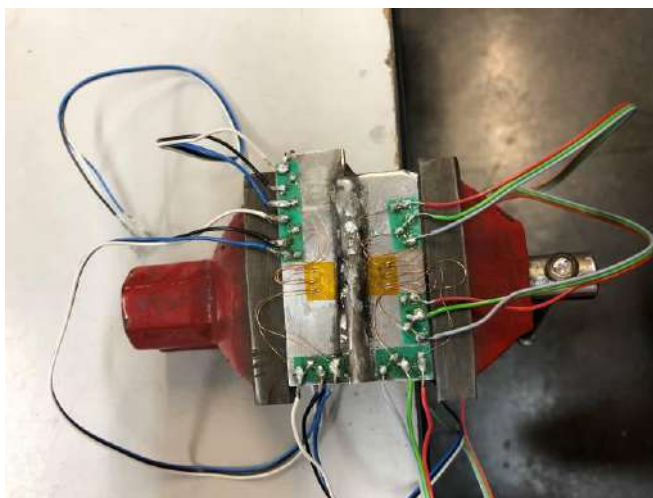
Detalhes do extensômetro colado na superfície da amostra com os fios soldados.
